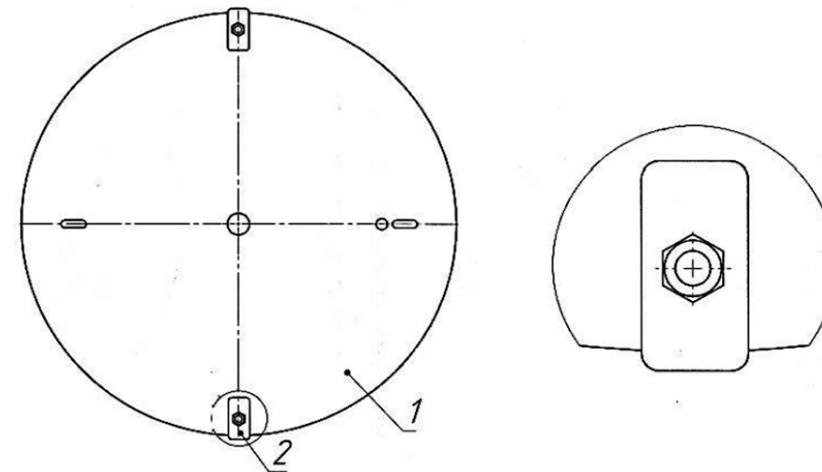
Нижняя стальная крышка устройства УЗЛ-Т ССД с установленными заглушками. 1 – диск; 2 – задвижка с болтом и гайкой, вид сверху. Гайка запорного механизма на рисунке не показана.
